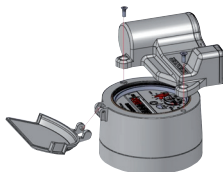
Montage des EDC-S auf Zähler mit Kupfer/Glas-Zählwerk (IP68)
